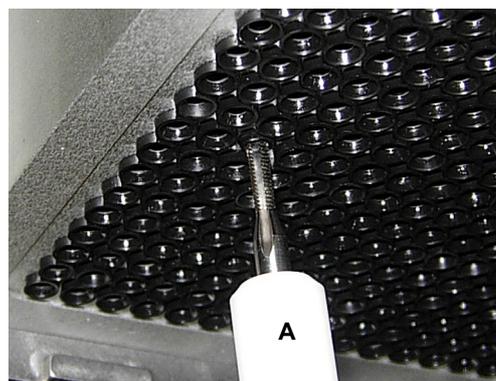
Ausbauwerkzeug für das stumpfe Rohr einsetzen
